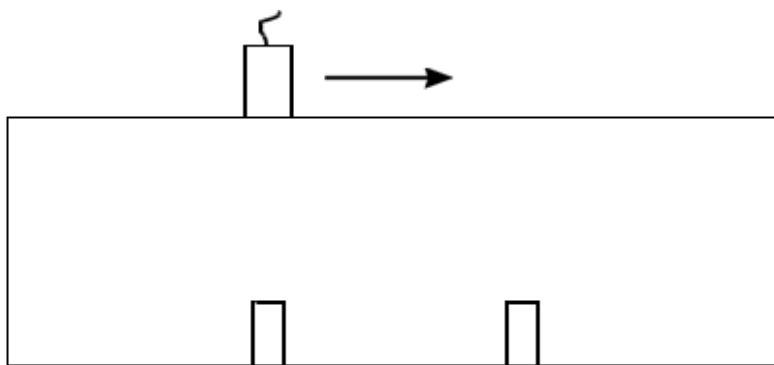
Образец с двумя отражателями, расположенными на одинаковой глубине
